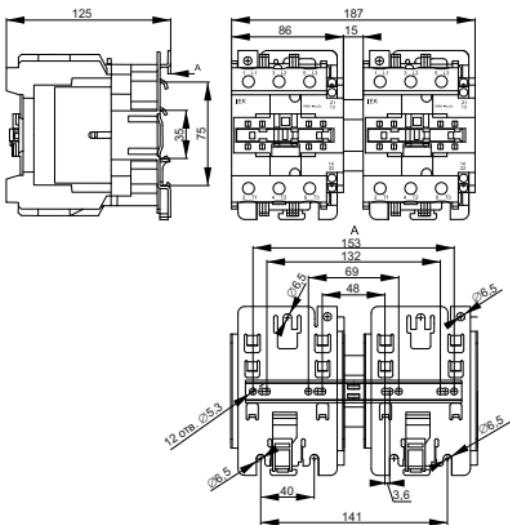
Габаритные и установочные размеры КМИ-48032, КМИ-49532 / Figure 6 – Overall and installation dimensions of KMI-48032, KMI-49532
